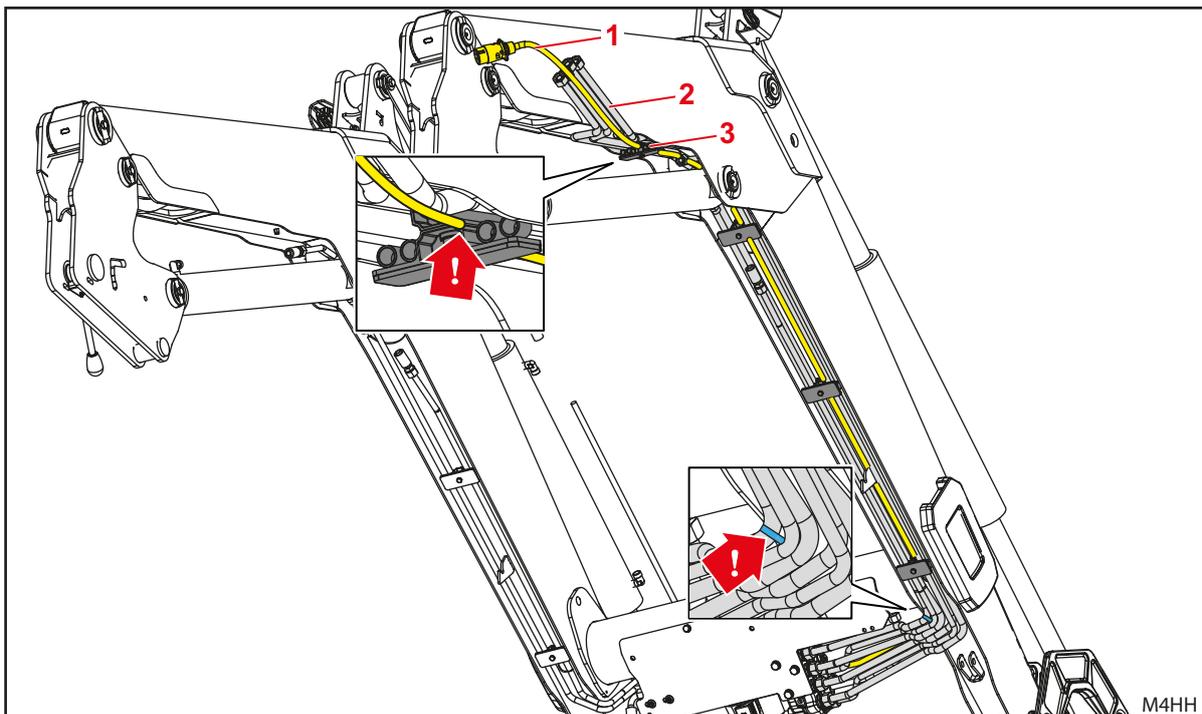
Panoramica – Posa del cavo del caricatore frontale
